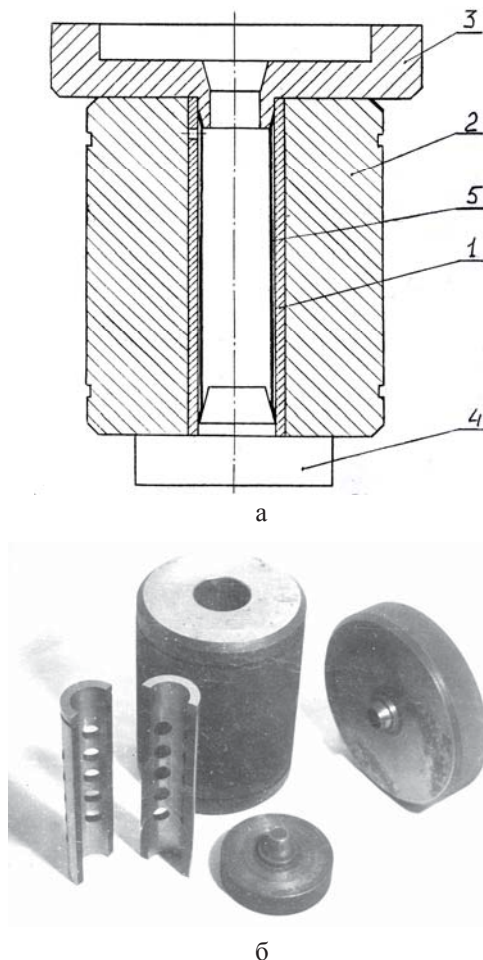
Оснастка для пробивки отверстий с расположением заготовки внутри матрицы: а – схема; б - внешний вид 1 – матрица, 2 – бандаж, 3 – опорное кольцо, 4 – основание, 5 – заготовка
